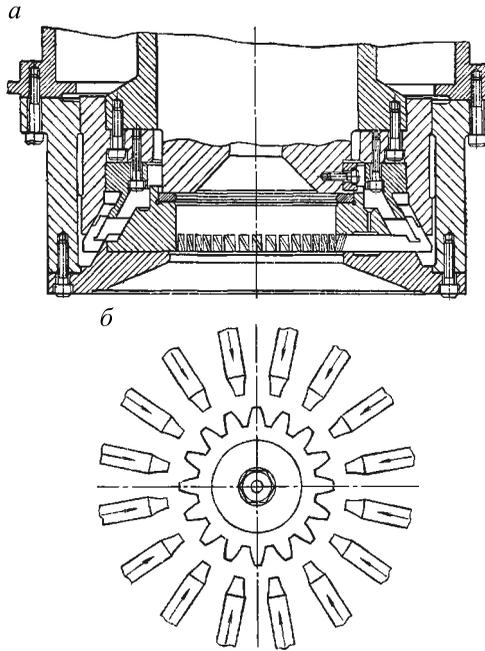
Схема зубодолбления специальной многорезцовой головкой
